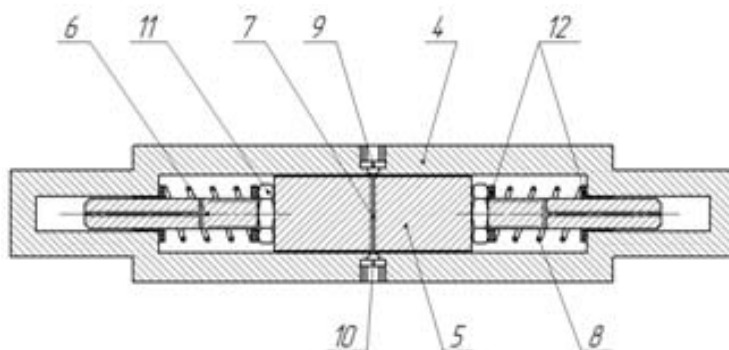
Вибродатчик: 4 – корпус; 5 – элемент; 6 – штырь; 7 – центральная прорезь; 8 – пружина; 9 – светозлучающий блок; 10 – приемный блок; 11 – регулировочная гайка; 12 – стопорные шайбы
